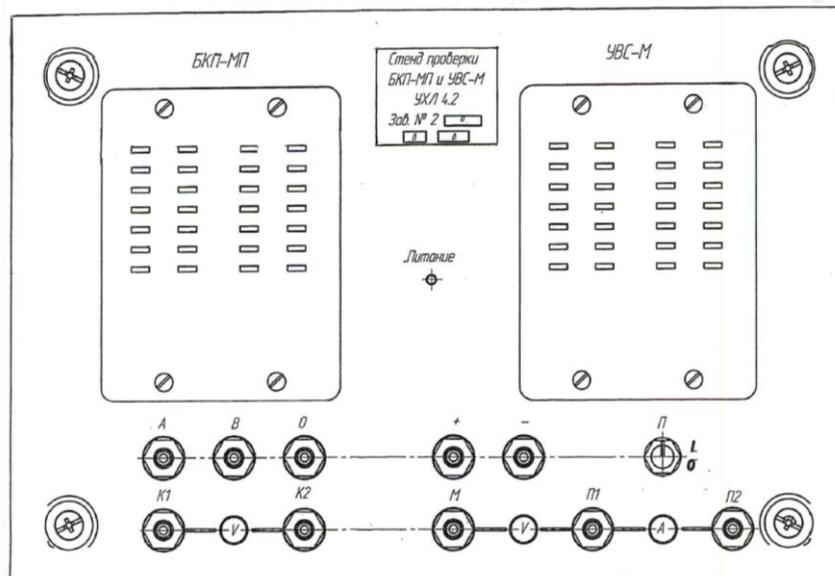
внешний вид стенда проверки БКП-МП и УВС-М
